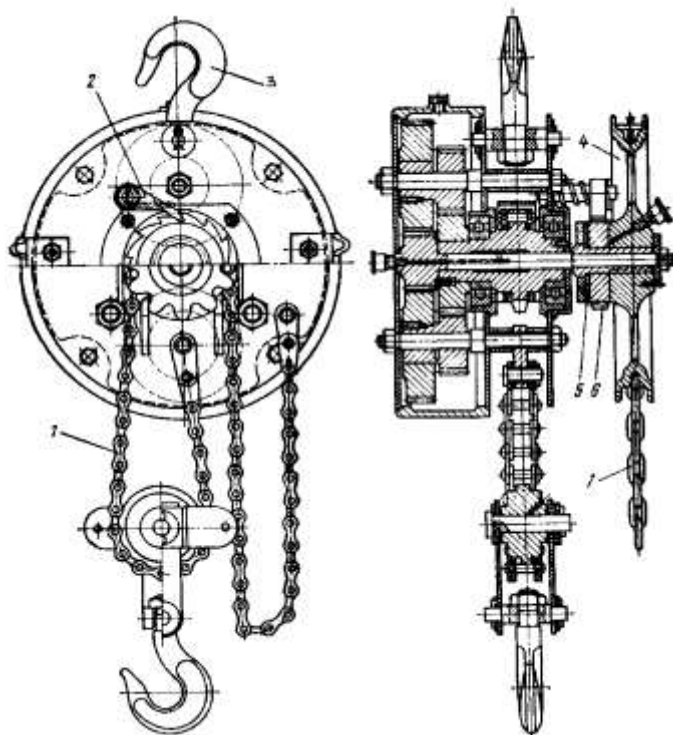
таль с ручным приводом с сосной зубчатой передачей
